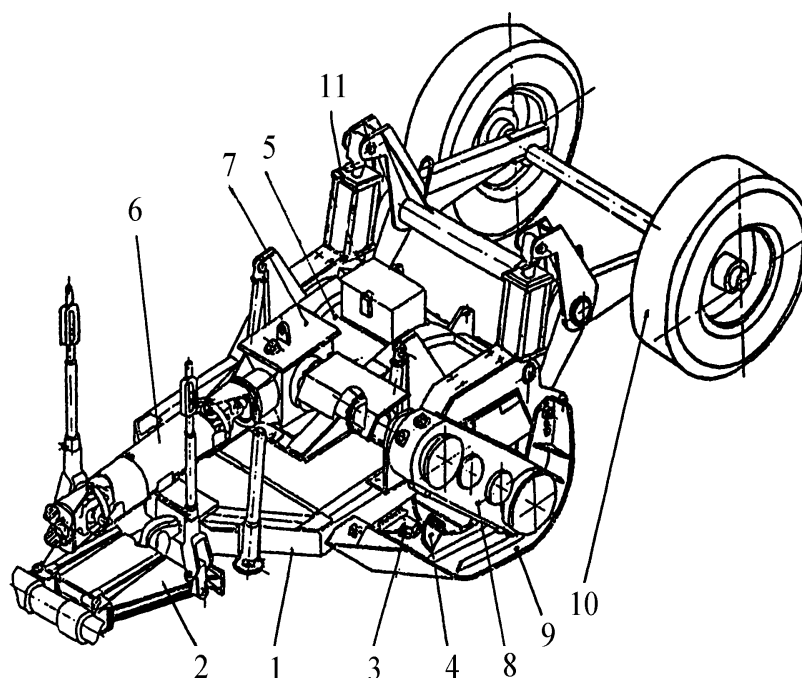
Машина лесная фрезерная МЛФ-0,8: 1 – рама; 2 – прицепное устройство; 3 – отбойная плита; 4 – фрезерный барабан; 5 – защитный кожух барабана; 6 – карданный вал; 7 – конический редуктор; 8 – боковой цилиндрический редуктор; 9 – опорные лыжи; 10 – колесные опоры; 11 – гидроцилиндры подъема машины
